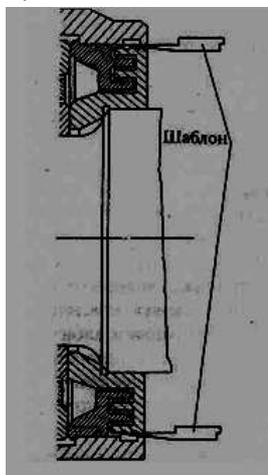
Схема проверки зазоров между лабиринтным кольцом и корпусом буксы.
